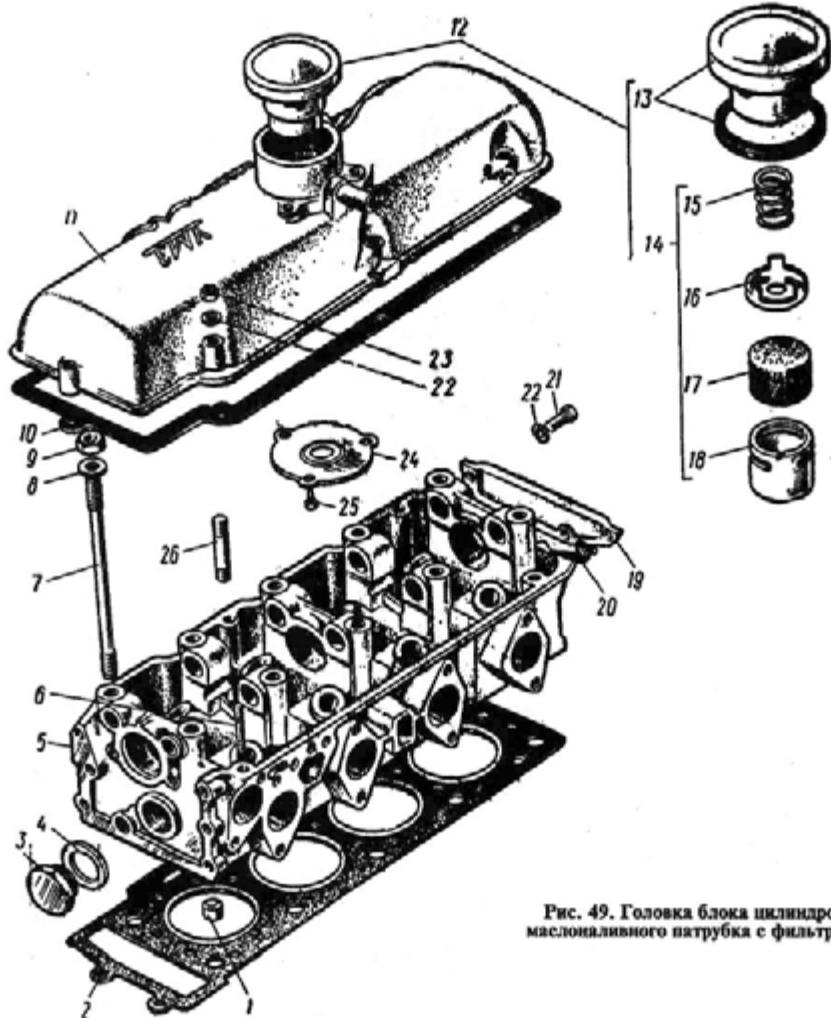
Головка блока цилиндров двигателя и пробка маслоналивного патрубка с фильтром вентиляции картера
